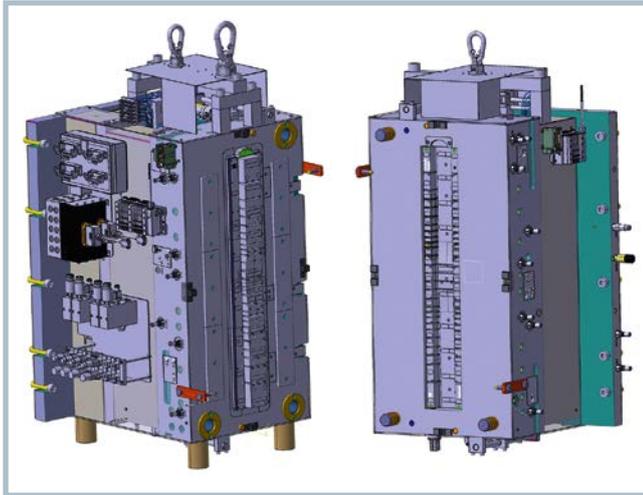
GKTool hat das Werkzeug für die Fertigung des Demonstratorbauteils konstruiert und gebaut; links: Stempel, rechts: Matrize (© GKTool)
